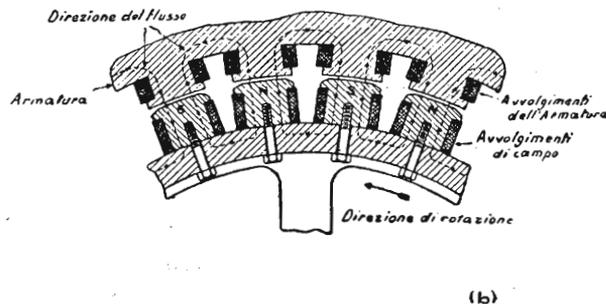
Dettaglio dell'alternatore a campo rotante.
